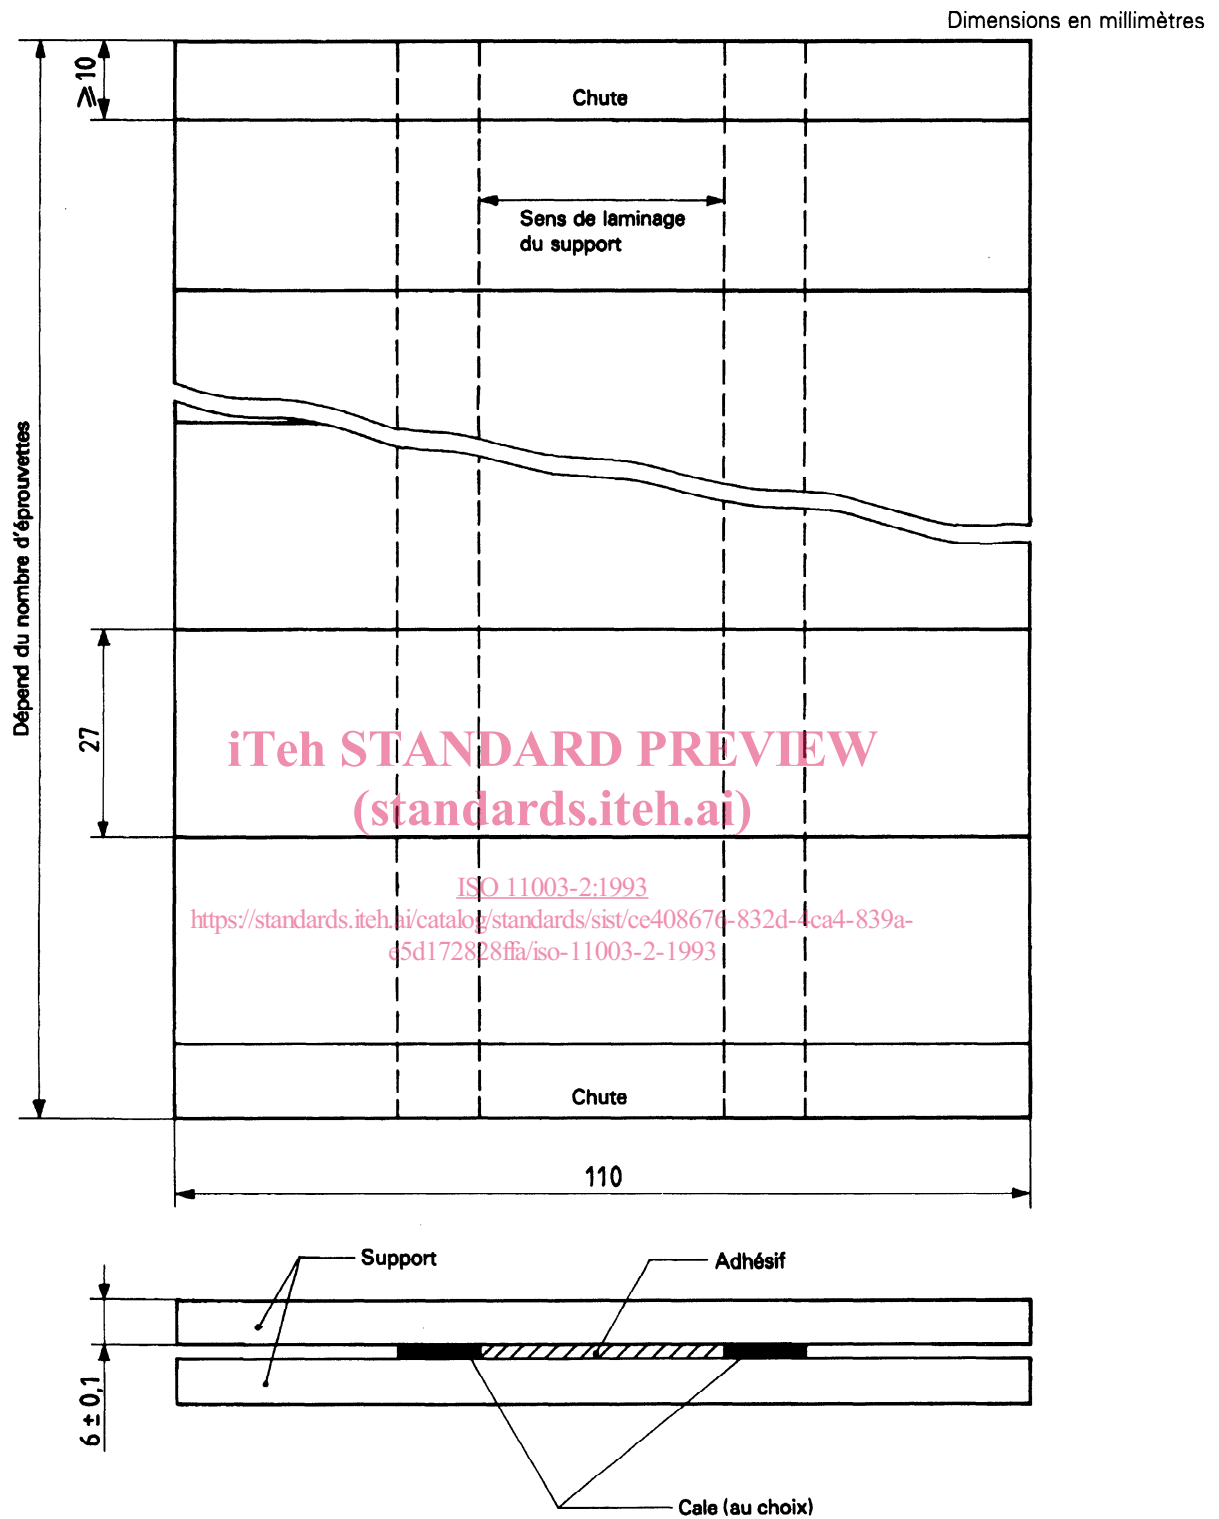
Panneau d'essai pour fabrication d'ensemble d'éprouvettes
